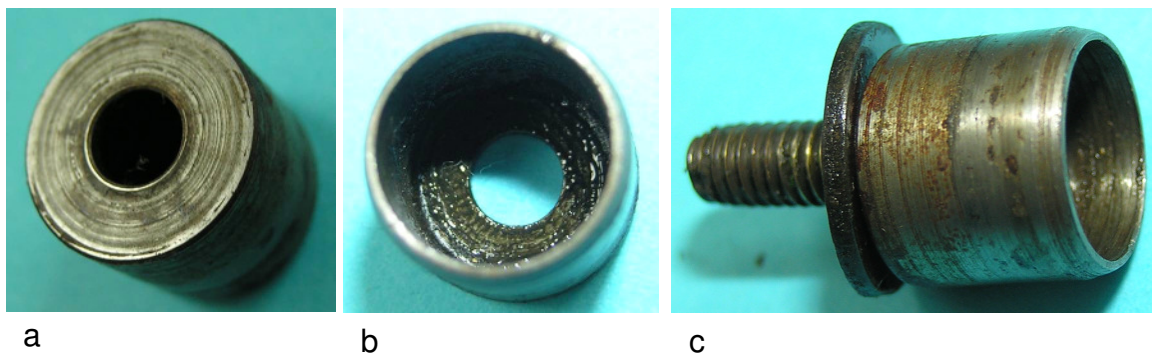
Ruhender Schleifring: a) Auf der Schalterkappe isoliert aufliegende Fläche, b) ringförmige Fläche als Kontaktfläche für den Kontaktbolzen, c) Schleifring mit Kontaktbolzen und Isolierung gegen die Schalterkappe
